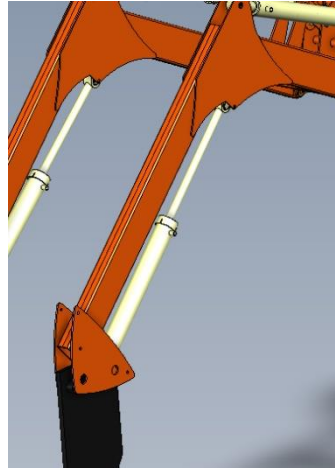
Viga 1 en la posición considerada para el cálculo. Inclinada 70° con la horizontal
